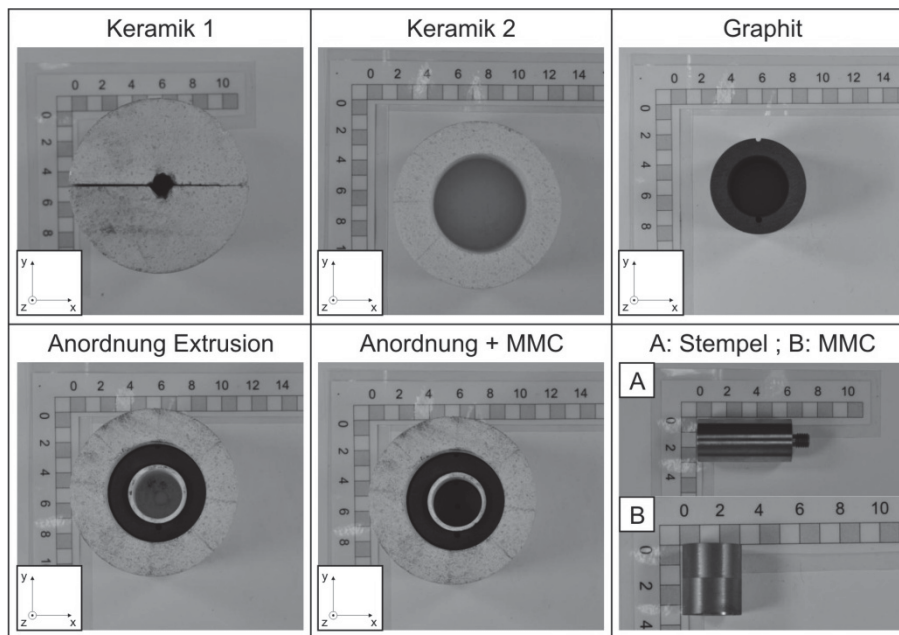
Werkzeuge für die Extrusion am Induktionsofen.
